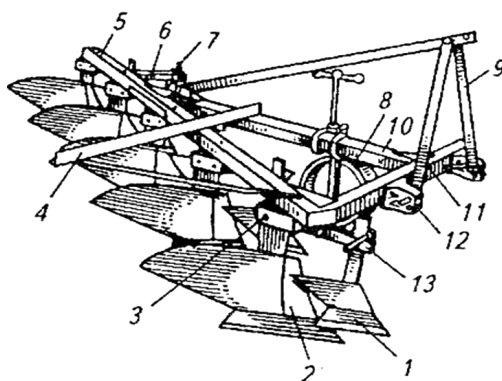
Общий вид плуга: 1 - предплужник; 2 - корпус; 3 - угольник; 4 - прицепка для бороны; 5 - главная балка; 6 - кронштейн крепления ножа; 7 - дисковый нож; 8 - опорное колесо; 9 - навеска; 10 - продольная балка; 11 - поперечная балка; 12 - кронштейн навески; 13 - кронштейн предплужника.
